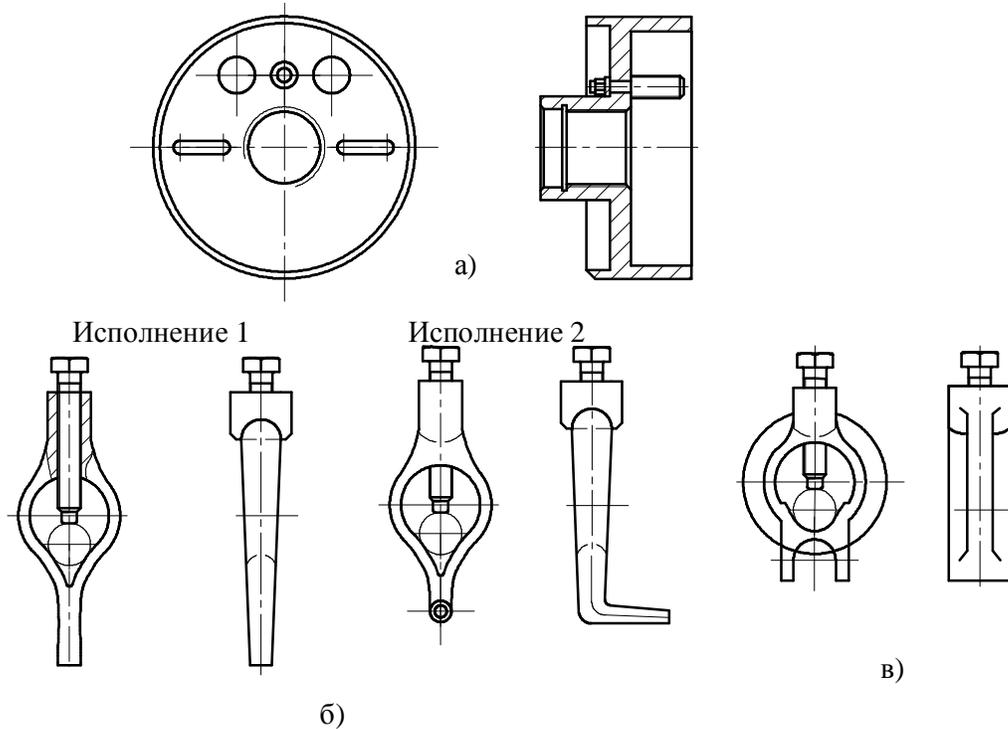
Поводковый патрон (а) и хомутики для токарных и фрезерных работ(б- для токарных и круглошлифовальных станков; в – для фрезерных станков)
